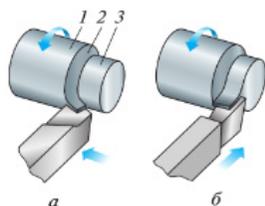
Движение резца и поверхности при токарной обработке:
